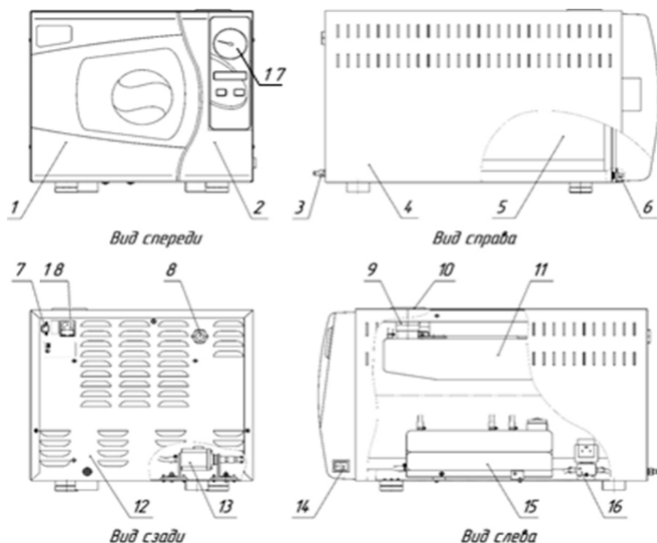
Внешний вид стерилизатора парового ГКа-25-ПЗ в варианте исполнения КИУС.942711.004-07.
